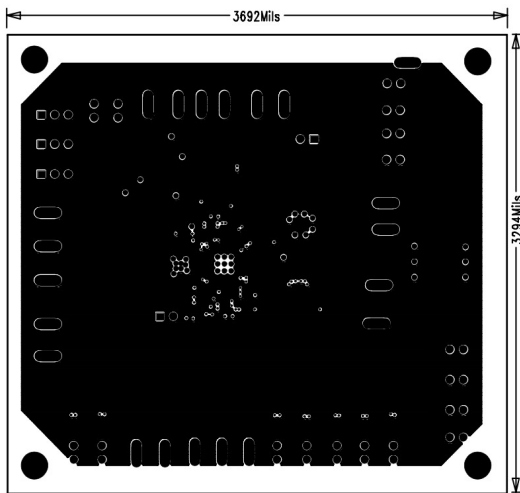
Max 8662 PCB LayOut - SYS Power Layer 3.
